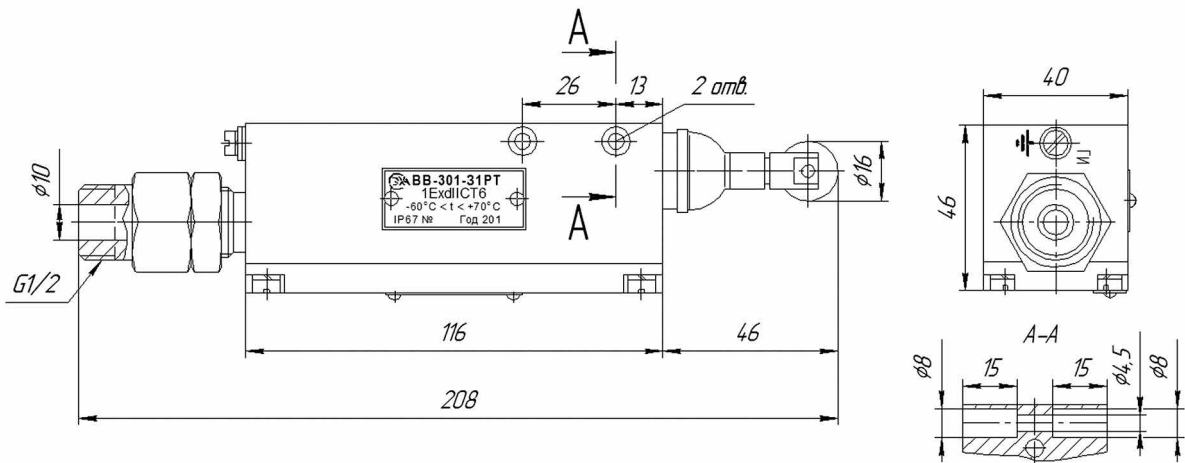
Габаритные и установочные размеры ВВ-301-31РТ
